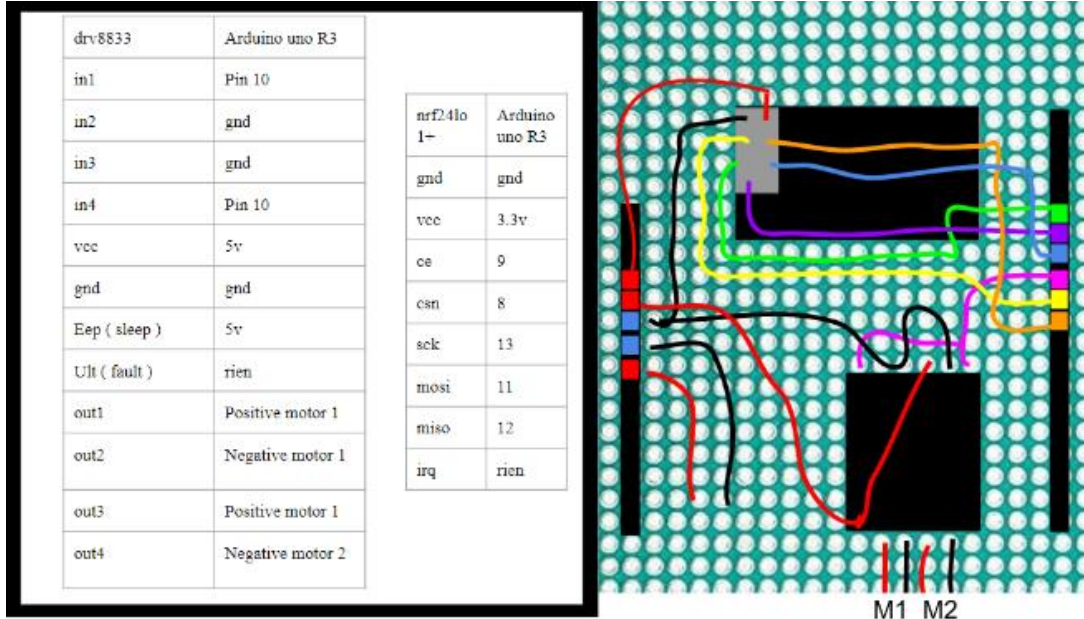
lien et soudage sur la protoboard de la partie motrice
